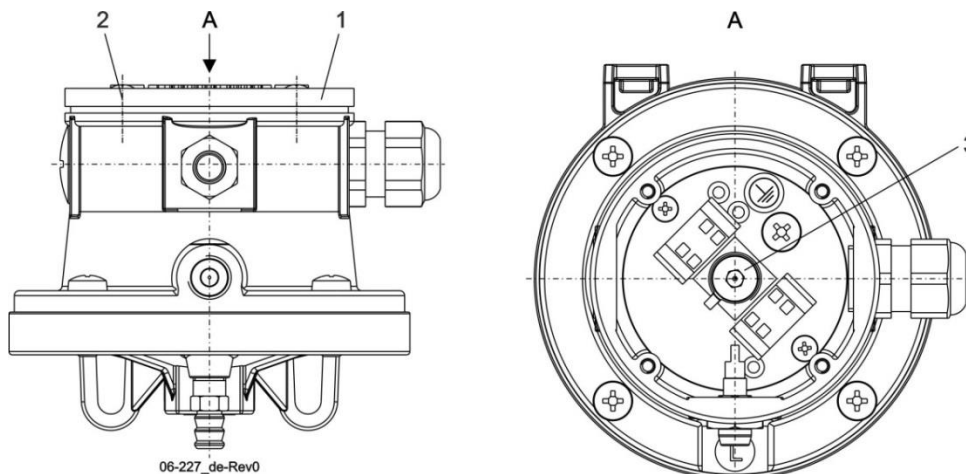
Einstellung des Schaltdrucks (Draufsicht ohne Anschlussraumdeckel)
